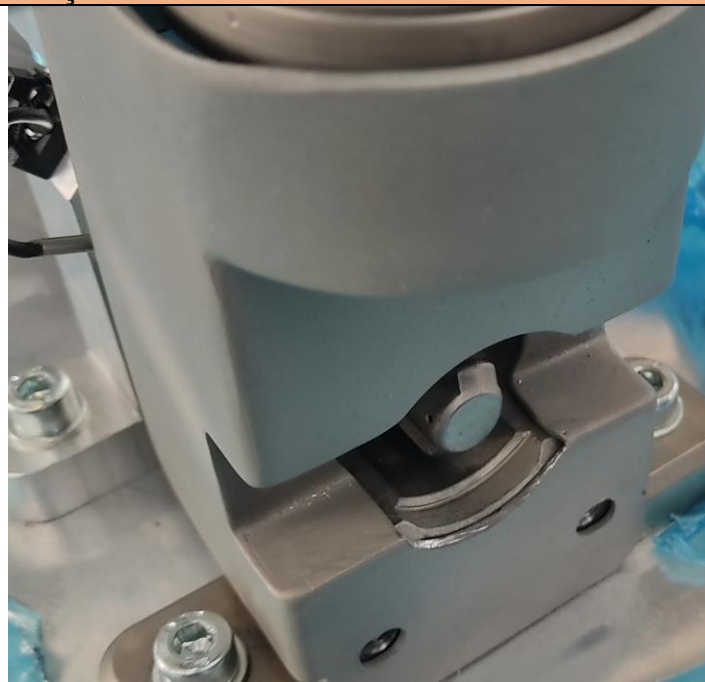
Aplicação da solução: proteção em Aço Jateado
